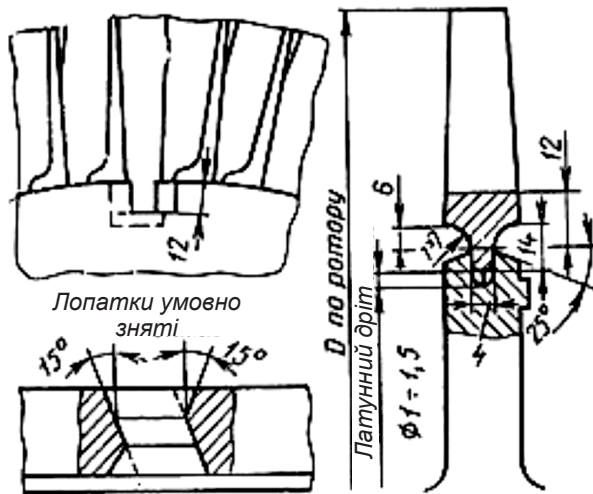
Ескіз обробки паза під корінь і хвостовик лопатки на диску робочого колеса турбіни турбокомпресора марки РДН-35
